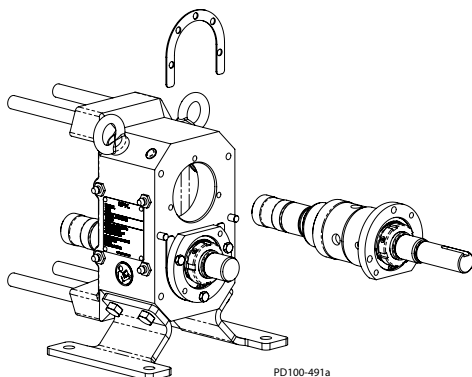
Zahnrad und Verriegelungsbaugruppe entfernen
